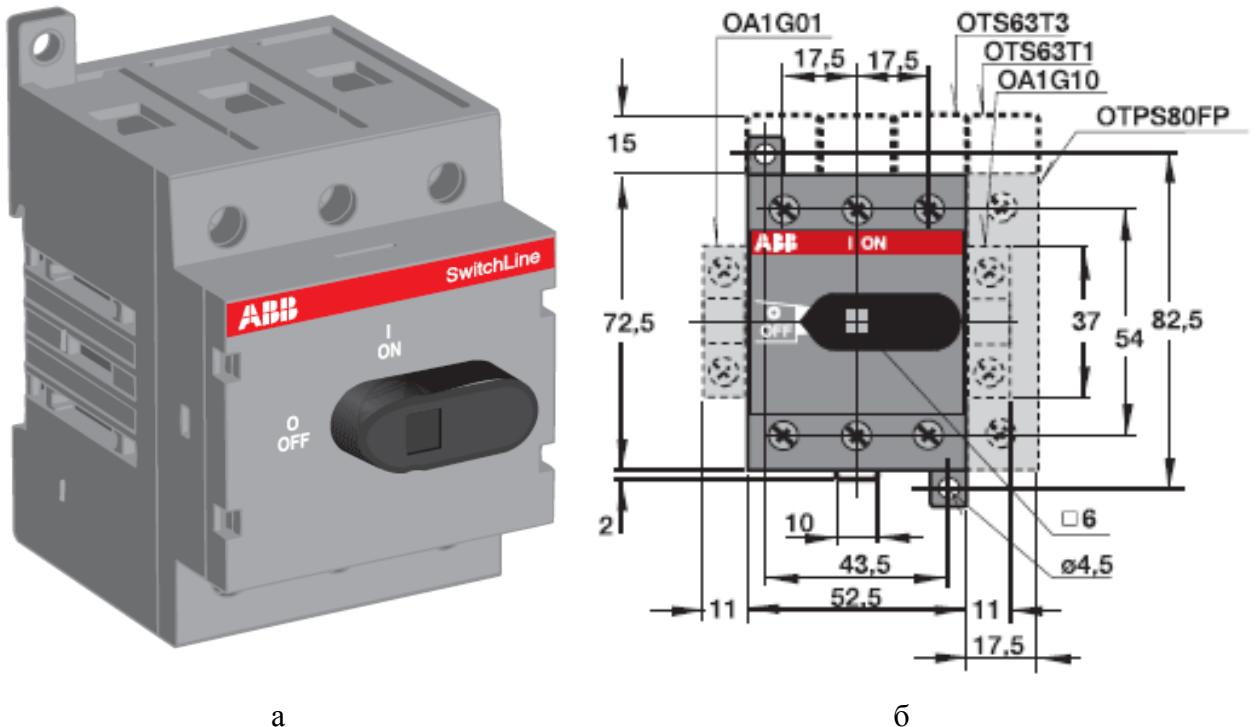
Общий вид разъединителя OT63F3 (а) и габаритные размеры(б).
